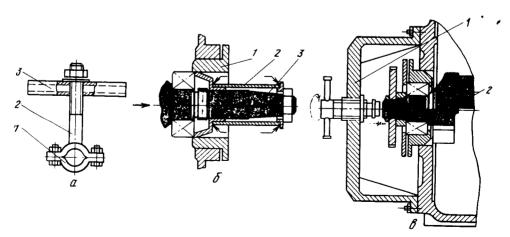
Приспособления, используемые при установке коленчатого вала:
